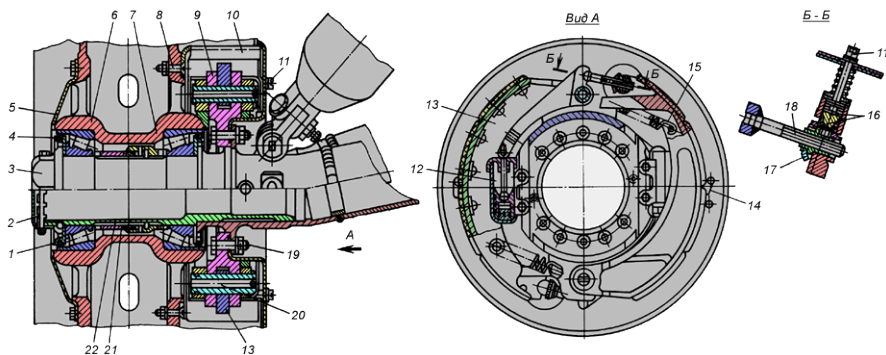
Барабан колеса КТ97 и тормозное устройство
